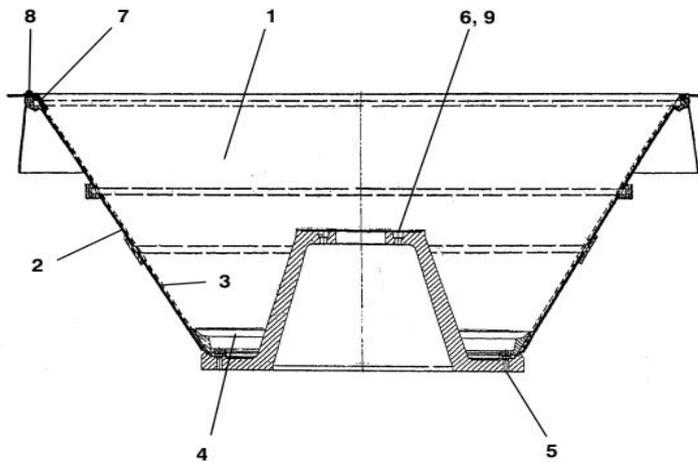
Dessin d'ensemble de la centrifugeuse
